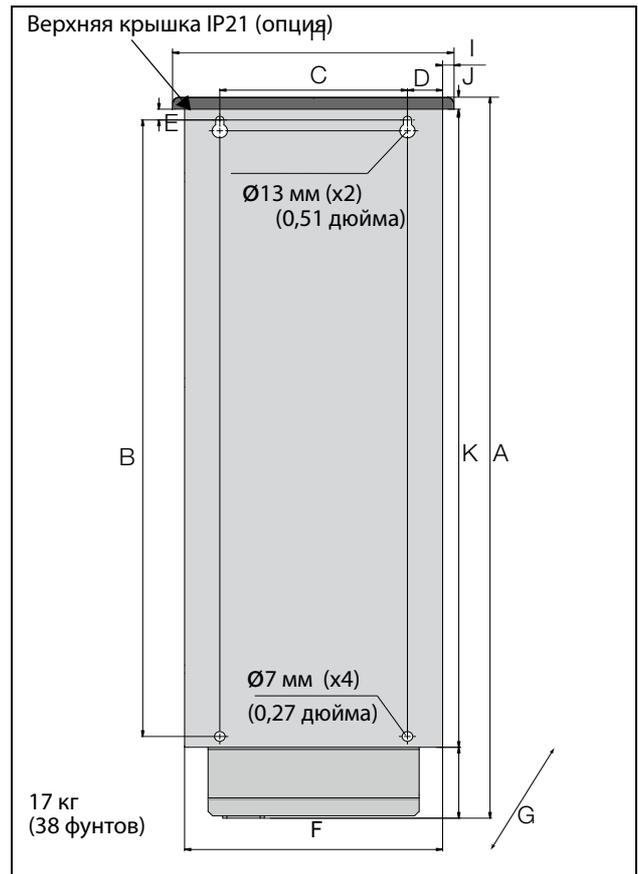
Устройство Emotron FDU моделей 48-025 по 48-058 (размер корпуса C2), моделей 69-002 — 69-025 (размер корпуса C2(69)), вид сзади.
